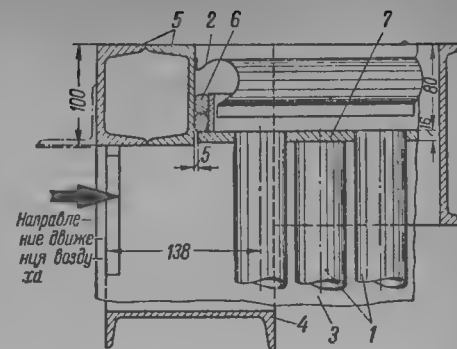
Сопряжение змеевикового экономайзера и трубчатого воздухоподогревателя. Под наклонными стенами происходит сильный золовый износ труб воздухоподогревателя.
